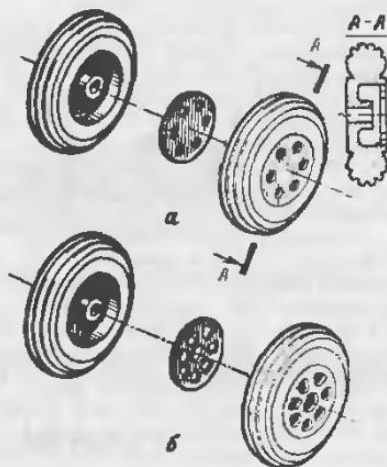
Колеса, изготовленные точением: а - с "дисками"; б - со "спицами"
